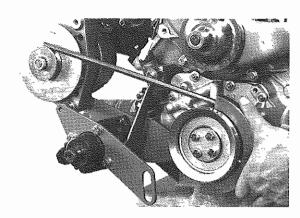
Allineamento pulegge albero motore-alternatore Alignment of crankshaft-alternator pulleys
